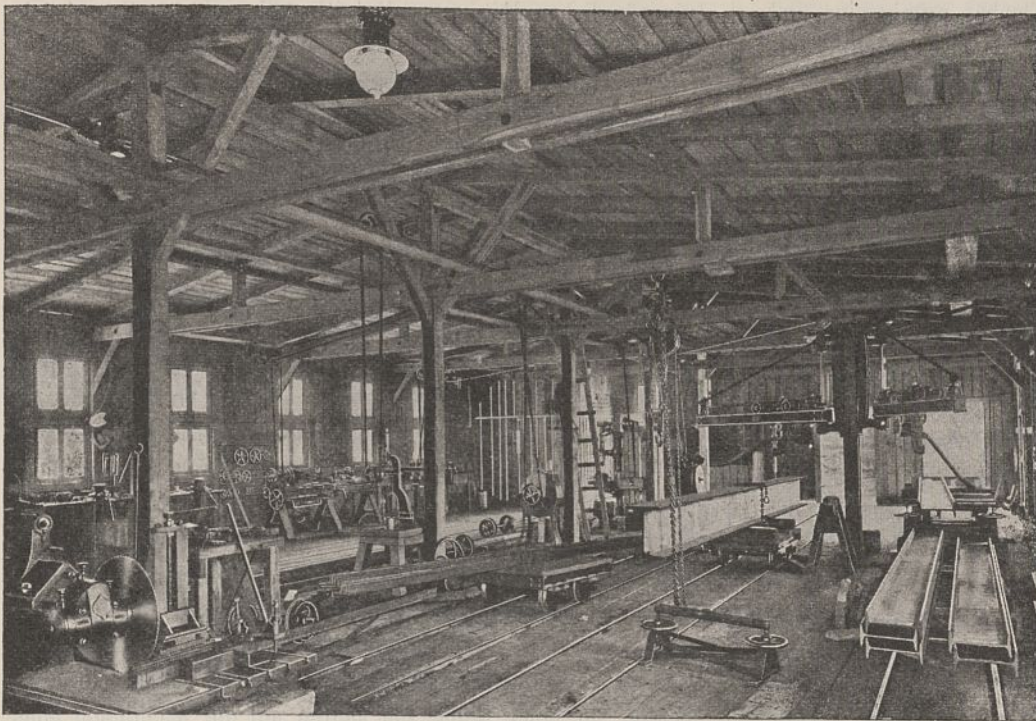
Werkstatt mit elektrischem Antrieb für die Bearbeitung des Tunnelleisens.
